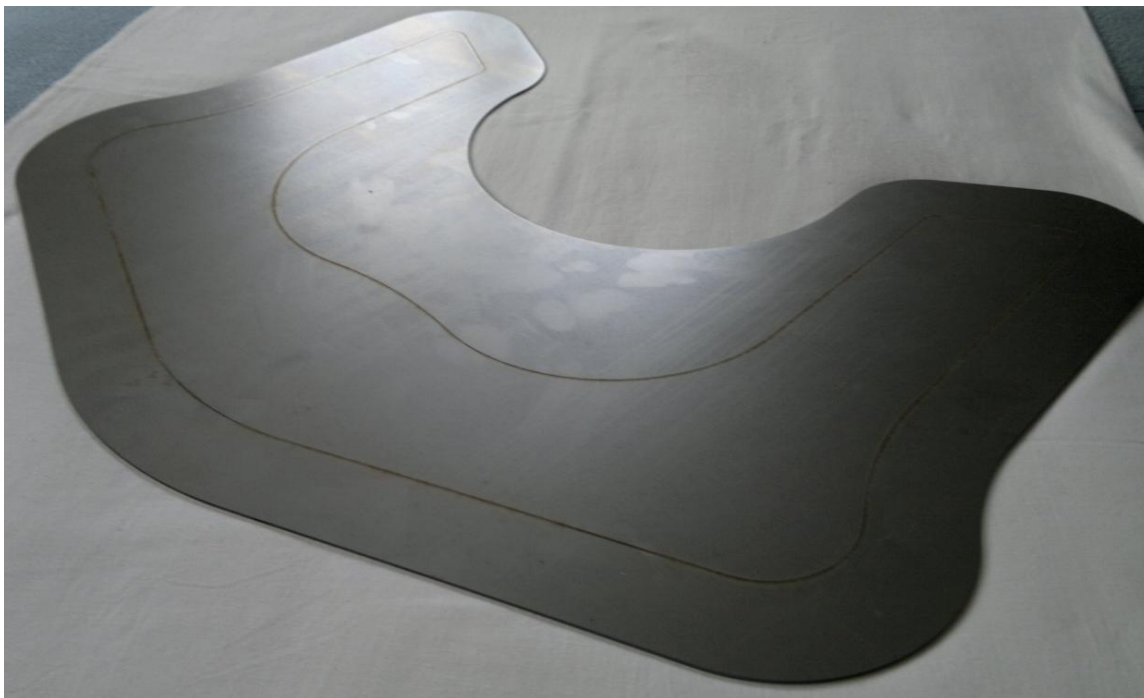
Detail vytvořeného obrysu pro ořezání výrobku
